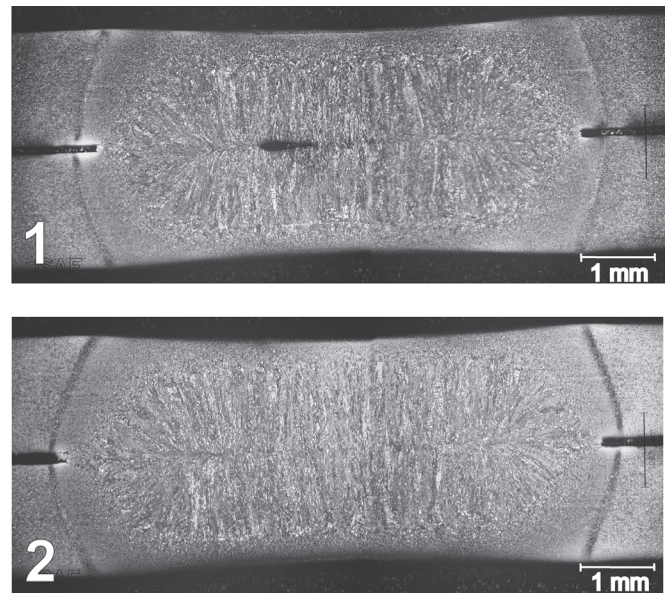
Makroaufnahmen von Punktschweißungen an 1,5 mm dicken MS 1200 +ZE mit (1) und ohne (2) Mittenlunker
